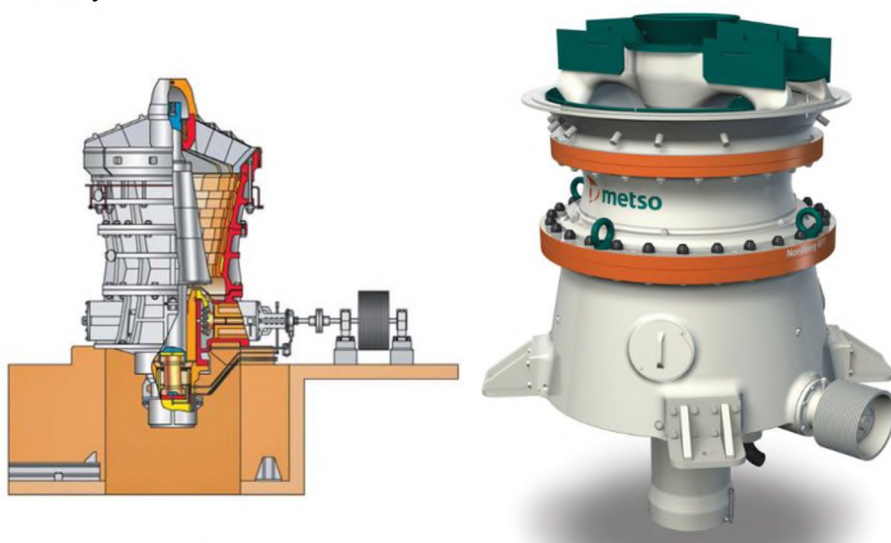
Конусная дробилка крупного дробления: конструкция и внешний вид
